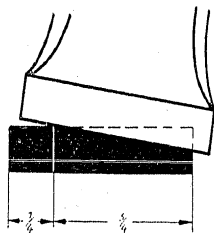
Verkanten des Hammers beim Schweißen
